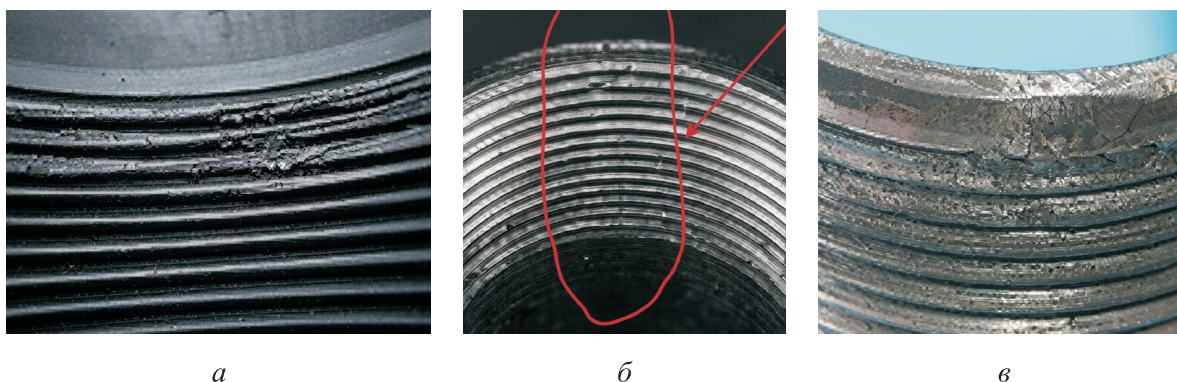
Схемы различных резьб корпуса ЭЦН:
